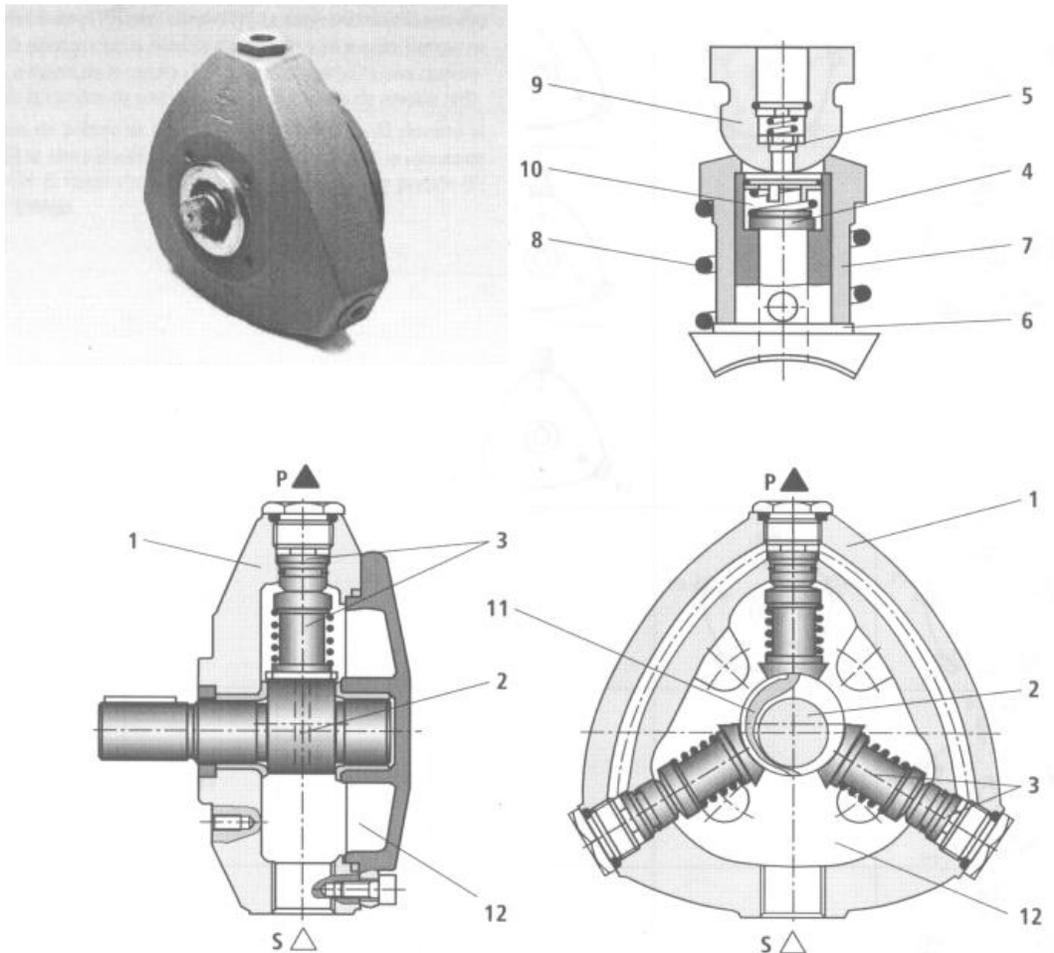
Bomba Circuito de Alta Presión: Pistones Radiales, Caudal Constante
